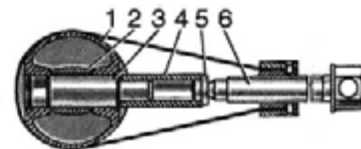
Запрессовка поршневого пальца в поршень и шатун с помощью приспособления 6999-7678:
